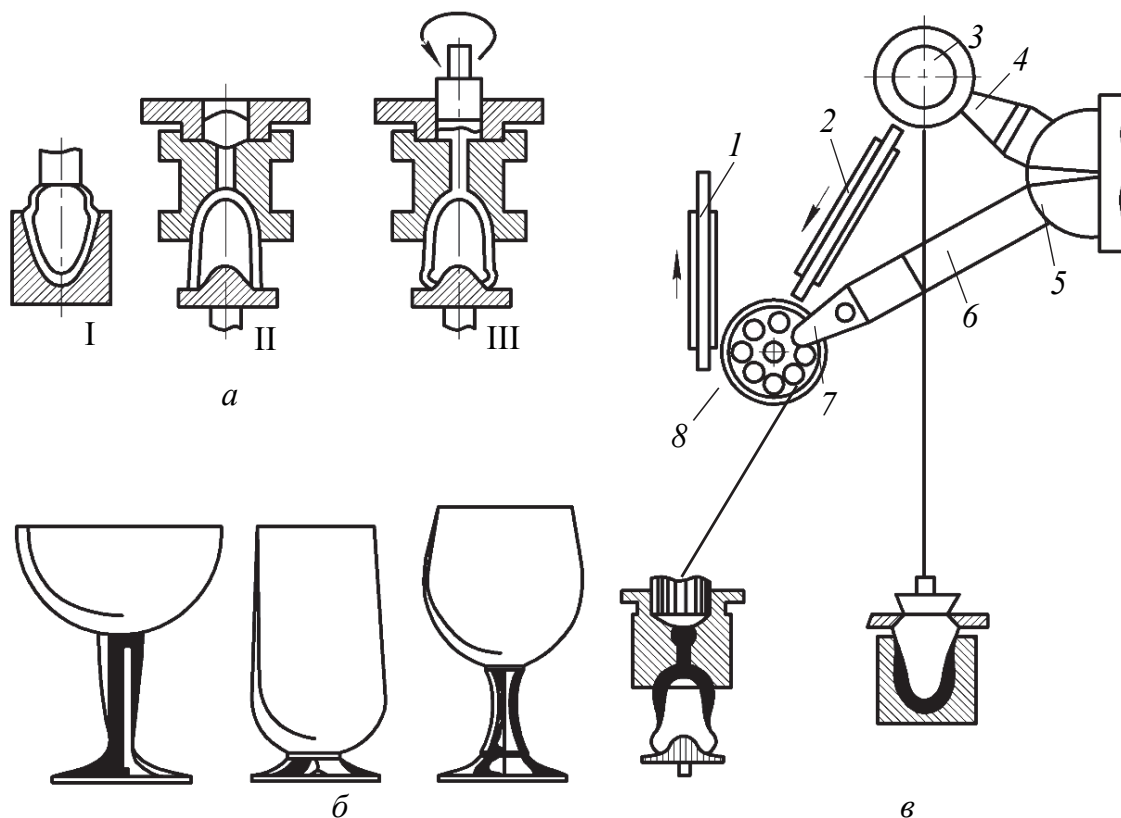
Схемы изготовления изделий на ножке (а), виды вырабатываемых изделий (б) и технологической линии для получения изделий с цветной ножкой (в);
